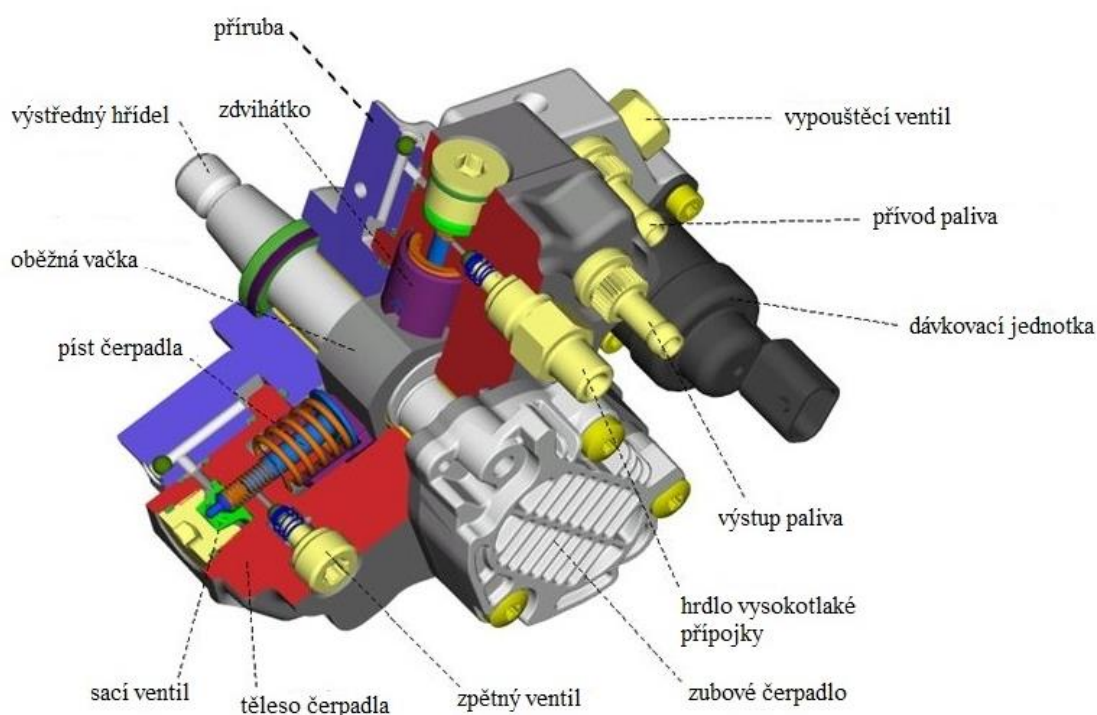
Radiální pístové erpadlo CP 1 [22]
